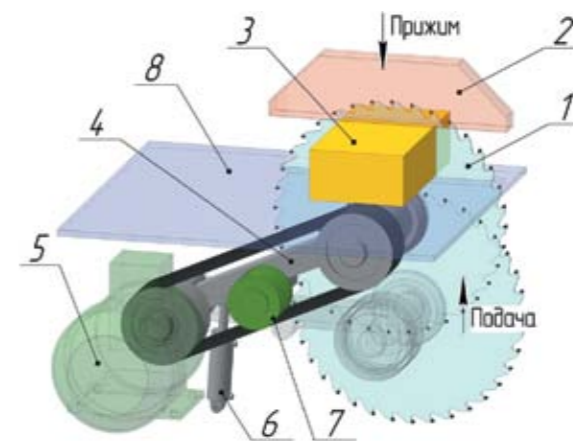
Торцовочный станок с вертикальной подачей: 1 – торцовочная пила; 2 – прижим-ограждение; 3 – заготовка; 4 – кронштейн со шпинделем; 5 – электродвигатель; 6 – исполнительный цилиндр; 7 – ременная передача с натяжителем; 8 – стол
